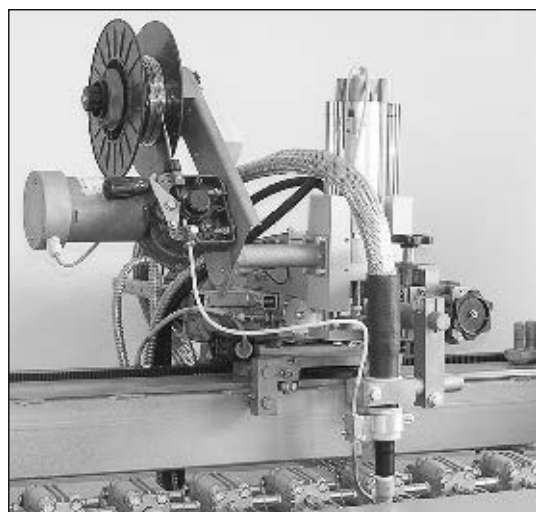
Устройство УП4 в составе автоматической установки АС303–2 для сварки продольных швов тонкостенных труб
